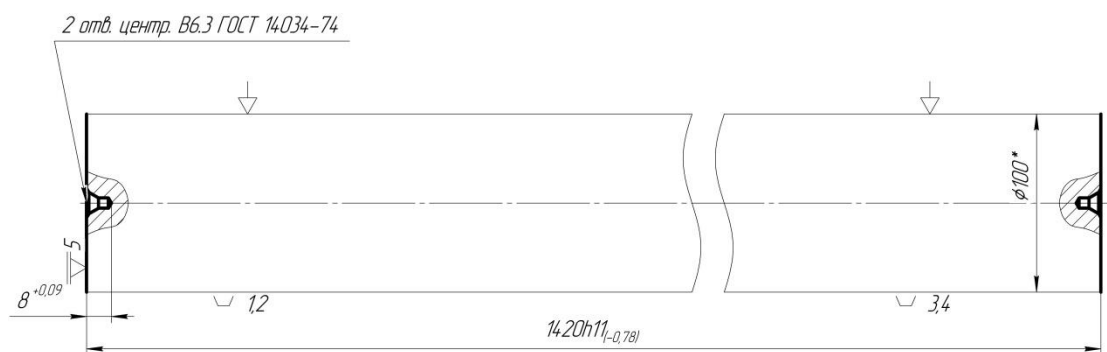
Схема установки заготовки на призми з притиском прихватами
